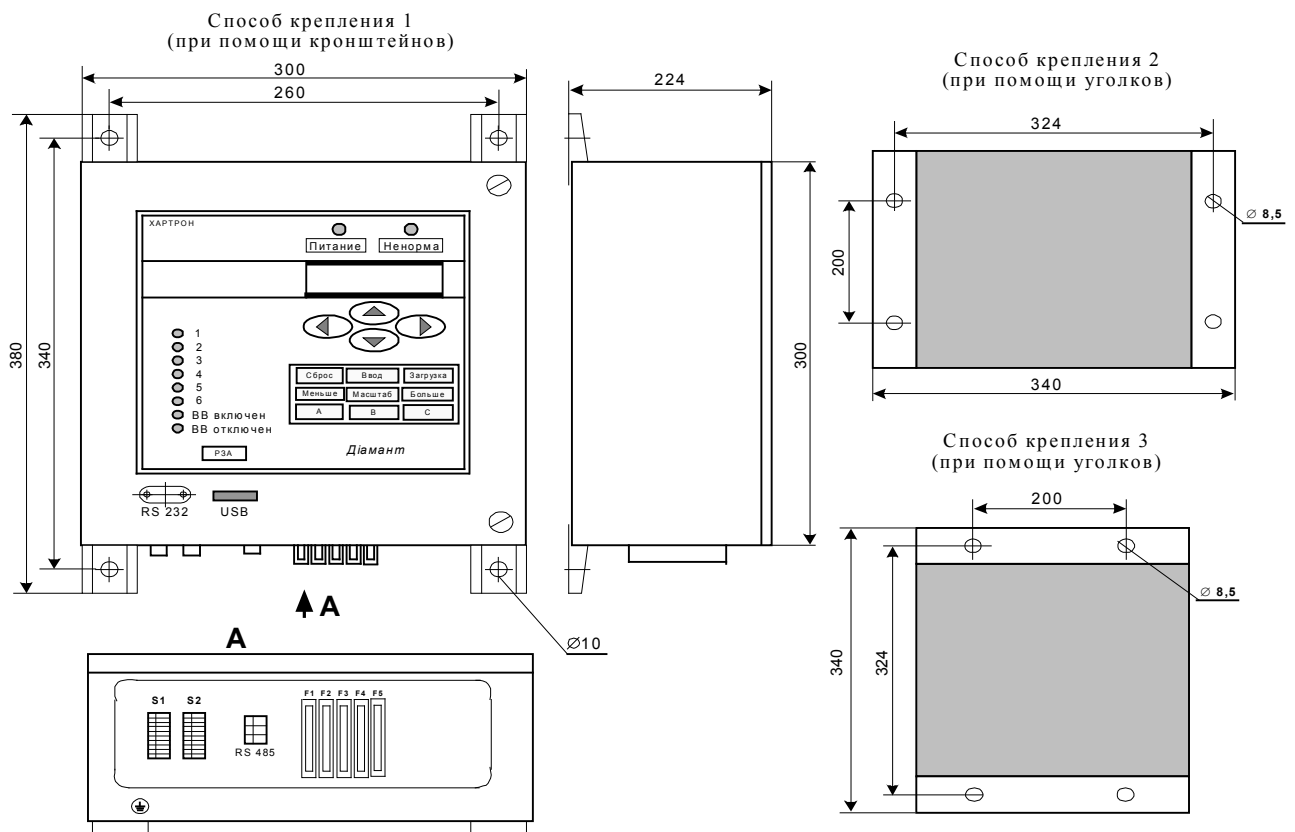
Габаритно – установочный чертеж ПМ РЗА
